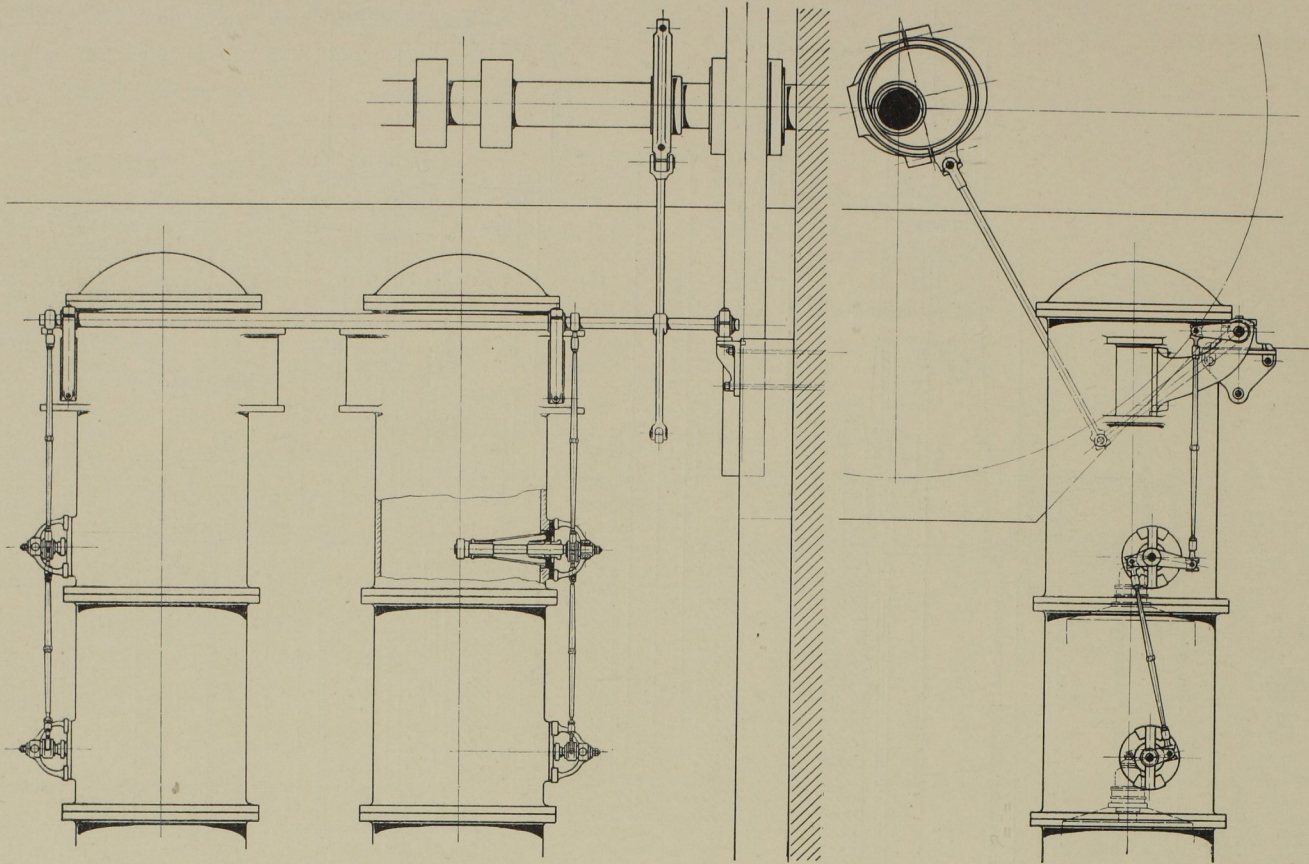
Pumpensteuerung. Masst. 1 : 50.
